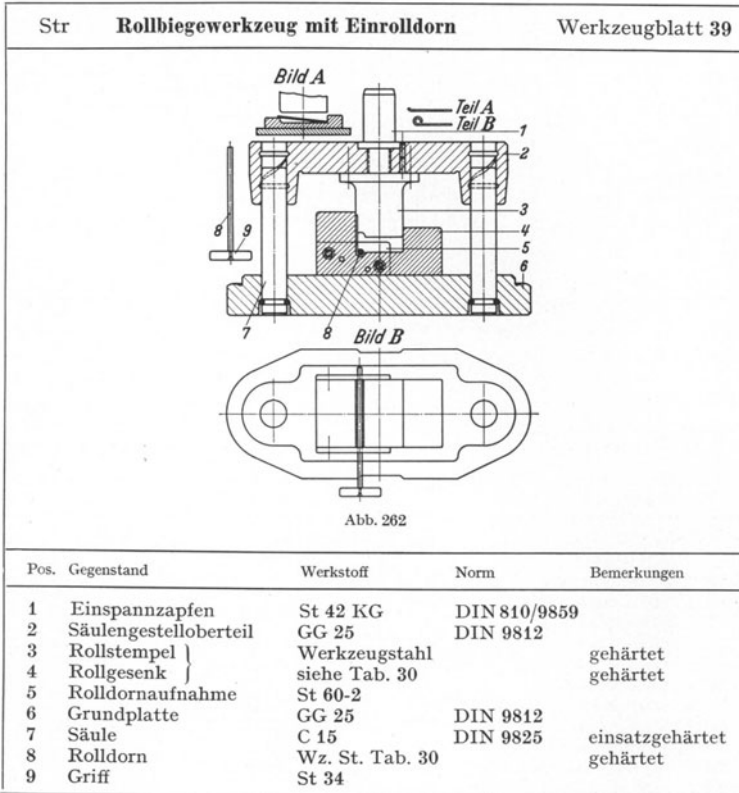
Bild A herzustellen. Denn die genaue Form der Anrolle ist für den Ausfall der Rolle in bezug auf den tolerierten Innendurchmesser ausschlaggebend. Werkzeugblatt 39 zeigt ein säulengeführtes Rollbiegewerkzeug mit Einrolldorn. Je ein halbes äußeres Rollenprofil im Stempel (Teil 3) und im Rollgesenk (Teil 4) gestatten ein Anrollen des Werkstückes über den Dorn (Teil 8). Der Dorn (Teil 8) wird in den seitlich angeschraubten Blechen (Teil 5) geführt. Nach dem Rollen wird der Rolldorn (Teil 8) herausgezogen, und das fertige Werkstück wird aus dem Werkzeug herausgenommen. Im Gegensatz zur Ausführung nach Werkzeugblatt 37 und 38 wird hier das Teil mit seiner Anrolle nach unten gelegt und so um den Dorn gerollt. Im oberen Teil des Werkzeugblattes 39 sind links zu Bild A das Prägewerkzeug, rechts das darin vorgebogene Teil A und darunter das Fertigteil B angegeben. Auf der Herstellung kleinster Rollen über Vorlochdorne von 0,8 mm Durchmesser wurde bei dem Folgeschnittwerkzeug zu Abb. 127 bereits hingewiesen.
